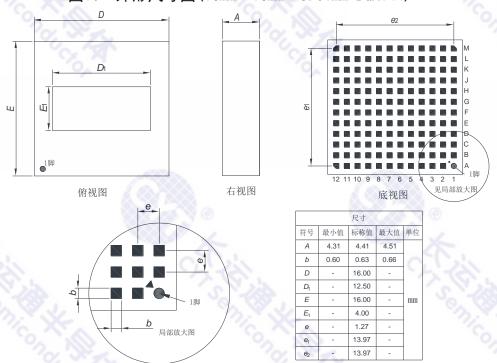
外形尺寸图 (16mm×16mm×4.41mm LGA144)
